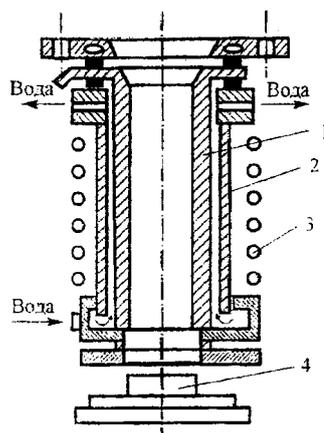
Схема изложницы: 1 - кристаллизатор; 2 - корпус; 3 - соленоид;
